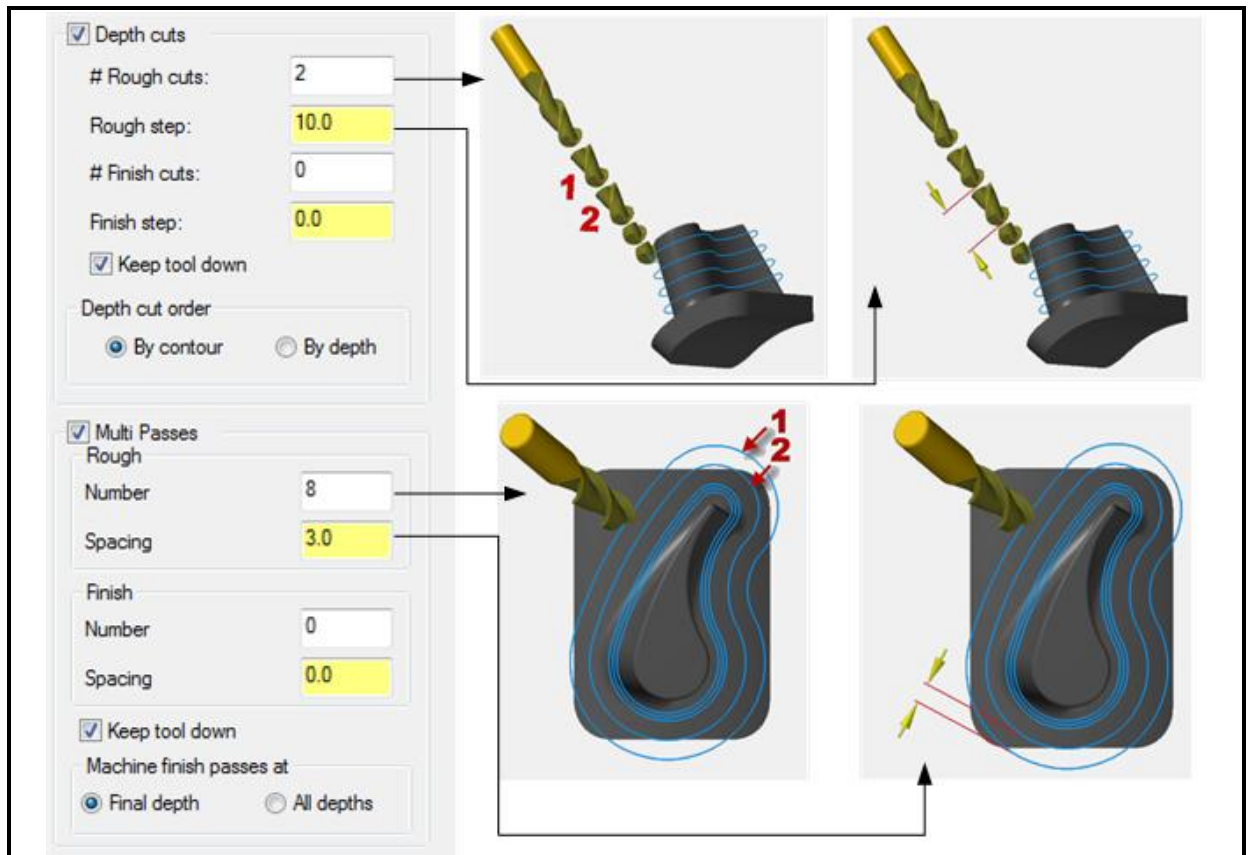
Volba obráběcího vzoru (*Cut pattern*) pro hrubovací operace
